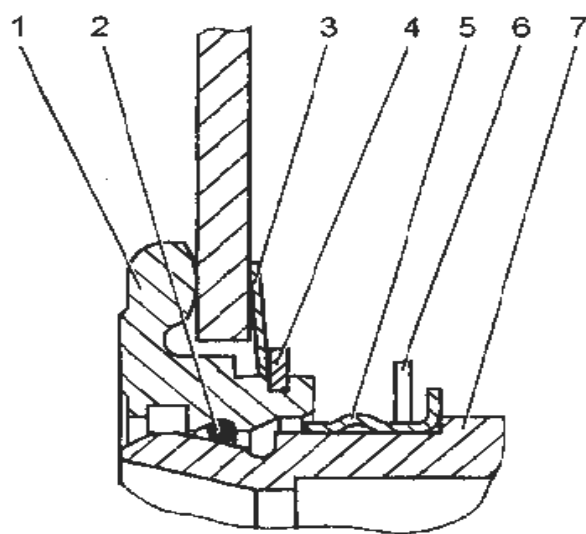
Запорное устройство: 1 – упорное кольцо; 2 – пружинное кольцо; 3 – пружинная шайба; 4 – стопорное кольцо; 5 – замковое кольцо; 6 – предохранительное кольцо; 7 – втулка подшипника
